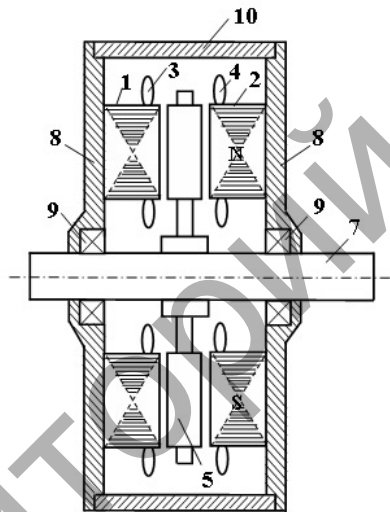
Низкооборотный торцевой генератор коммутаторного типа (НТГК-1)
